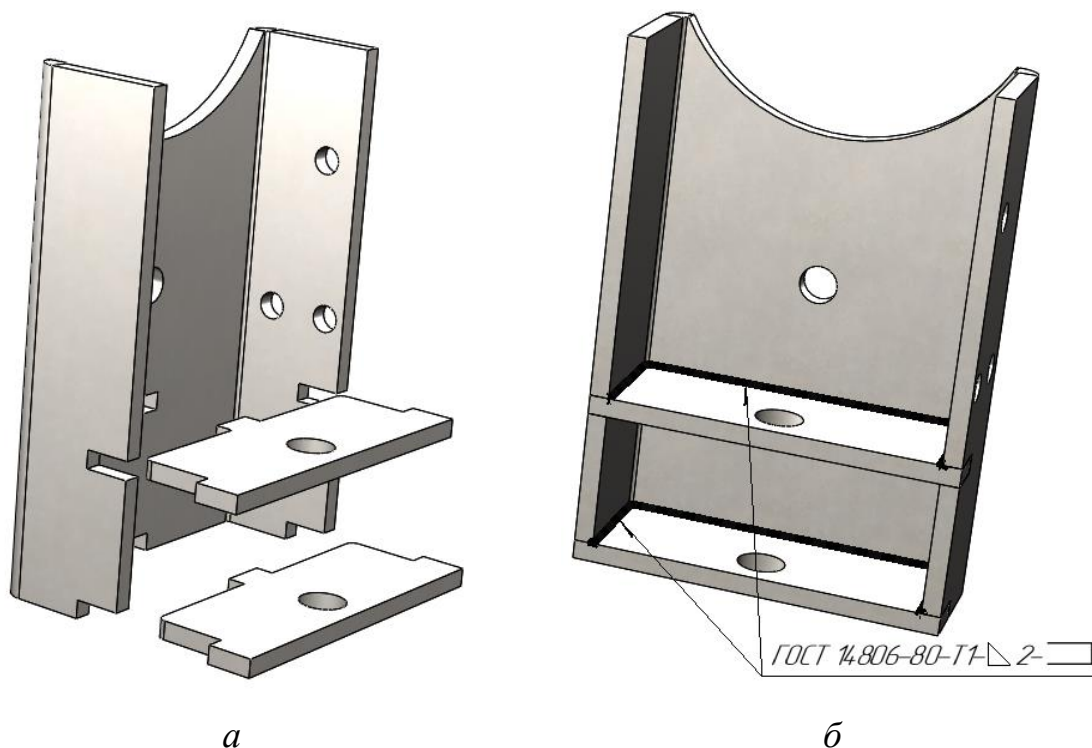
Сборка нижней части переднего поворотного кулака: *а* – общий вид сборки; *б* – сварное соединение деталей.
